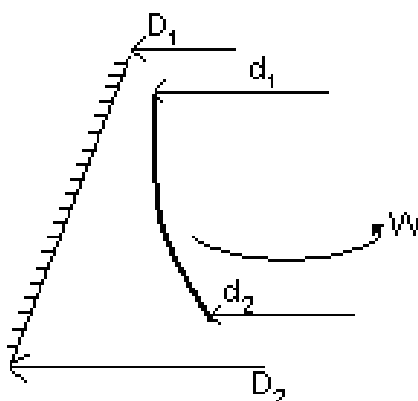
Конструкція з конічною формою твірної кожуха та параболічною формою твірної шнека
